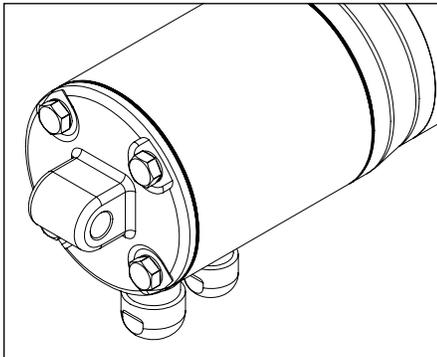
PCD: hintere Gabelkopfbefestigung optional erhältlich PCDR: hintere Gabelkopfbefestigung um 90° gedreht
